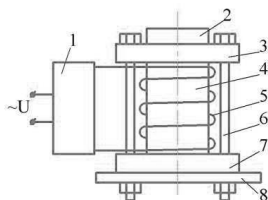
Схема п'єзоелектричного високочастотного перетворювача: 1-генератор високої частоти; 2-робоча поверхня перетворювача; 3,7-металеві накладки; 4-набір п'єзопластин; 5-обмотка; 6-стяжні гвинти; 8-основа
